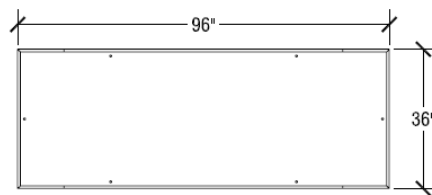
ENTARIMADO METÁLICO DE PIERNA PLEGABLE 3' X 8' ALTURA MÚLTIPLE
